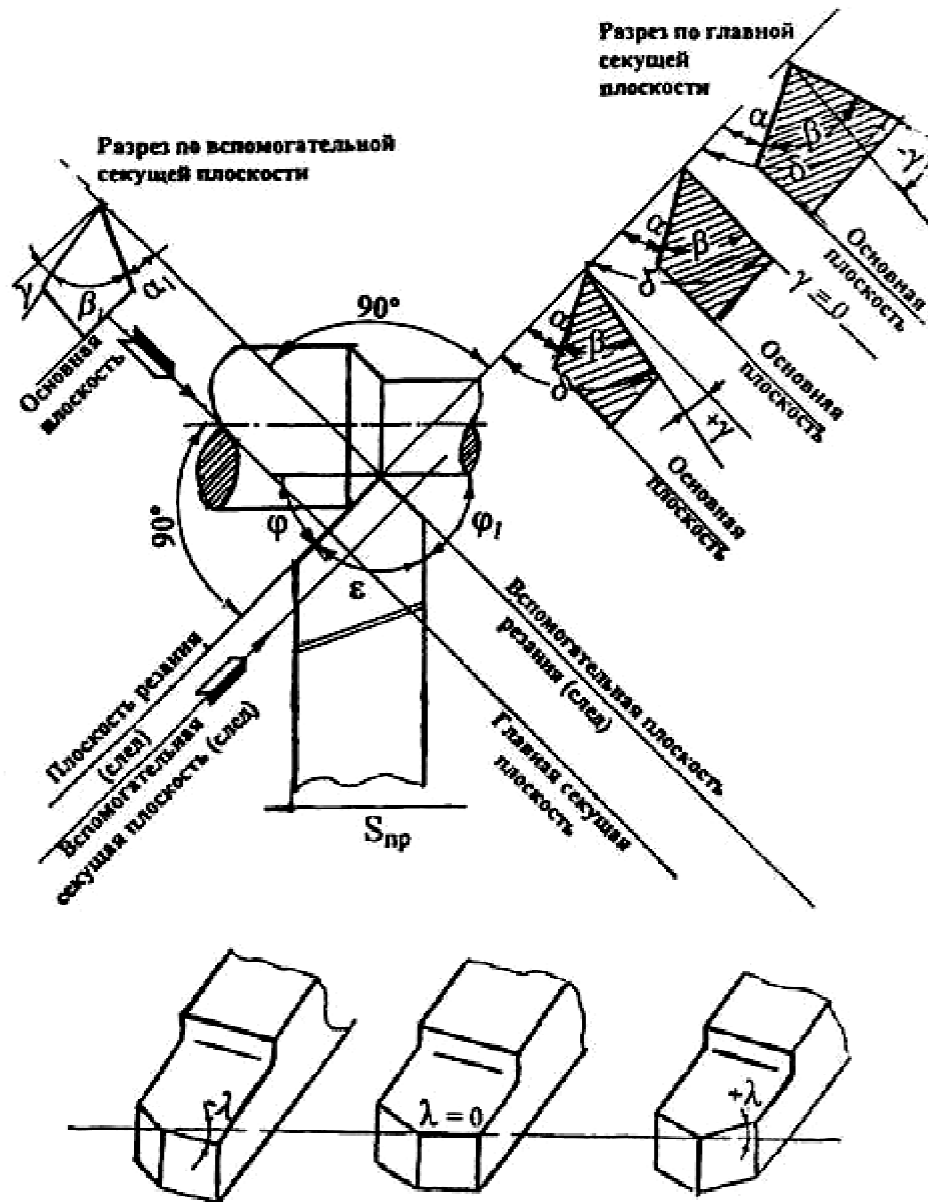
Основные поверхности заготовки и координатные плоскости
